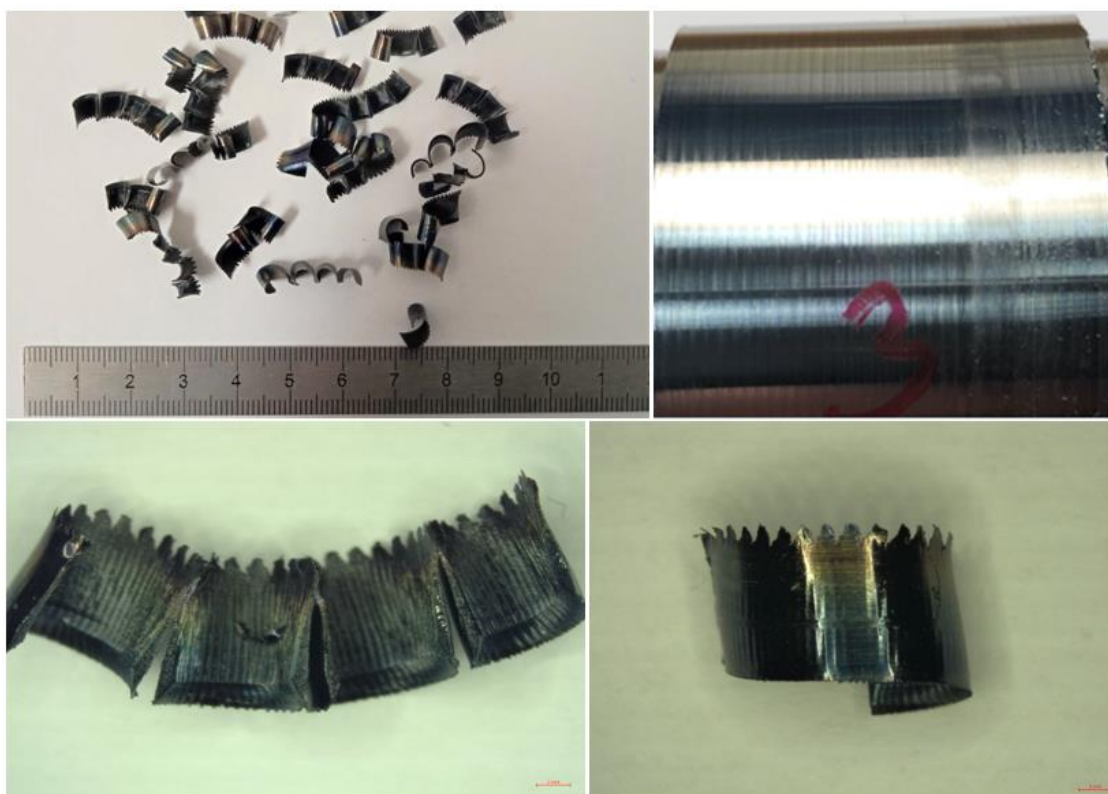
Třísky a obroběný povrch, VBD 1.
